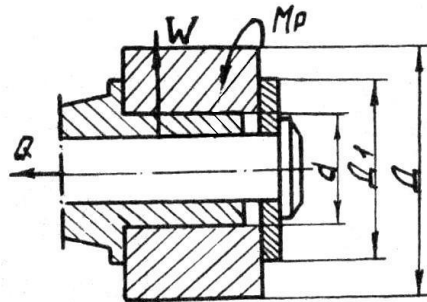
Схема установки заготовки на консольну жорстку оправку з торцевим затисканням
